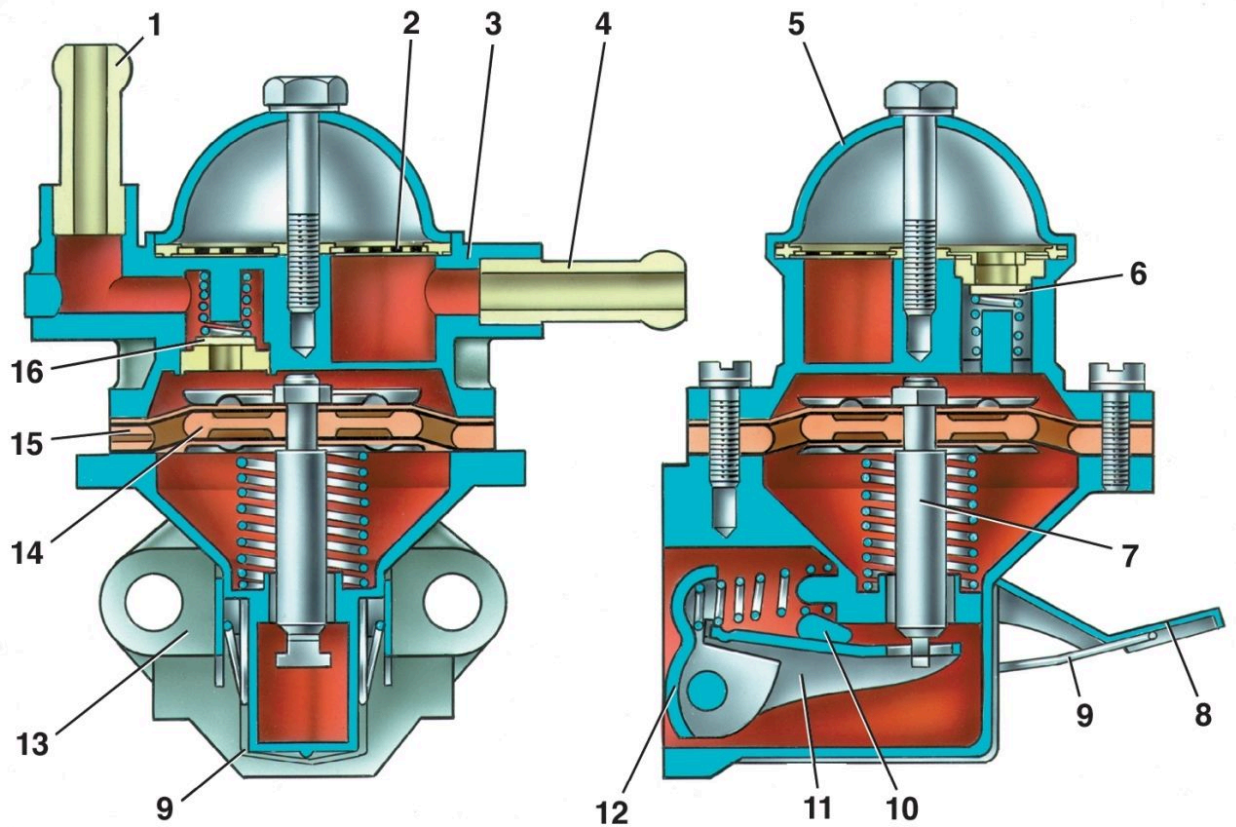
Паливний насос: 1 - нагнітальний патрубок; 2 - фільтр; 3 - корпус; 4 - усмоктувальний патрубок; 5 - кришка; 6 - всмоктувальний клапан; 7 - тяга; 8 - важіль ручного підкачування; 9 - пружина; 10 - ексцентрик; 11 - балансир; 12 - важіль механічного підкачування; 13 - нижня кришка; 14 - внутрішня дистанційна прокладка; 15 - зовнішня дистанційна прокладка; 16 - нагнітальний клапан
